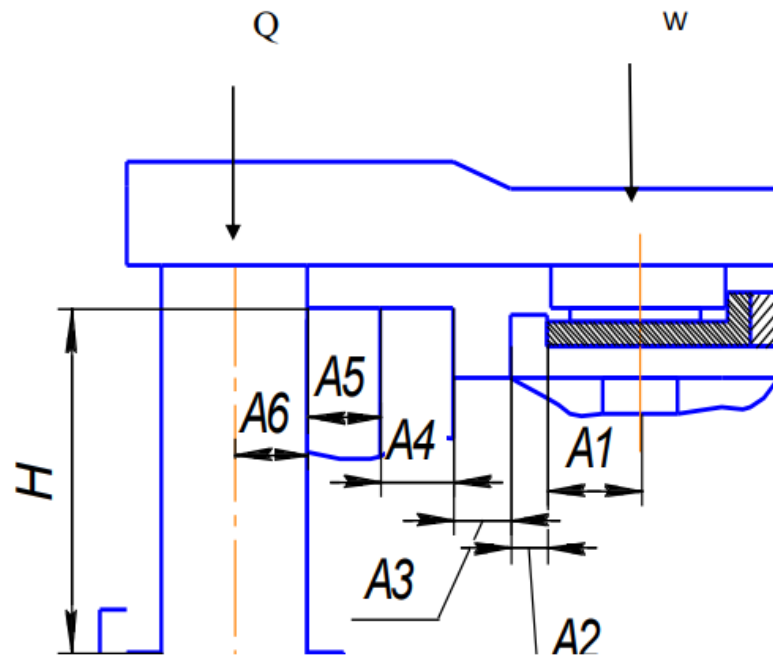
Схема закріплення заготовки в кондукторі
